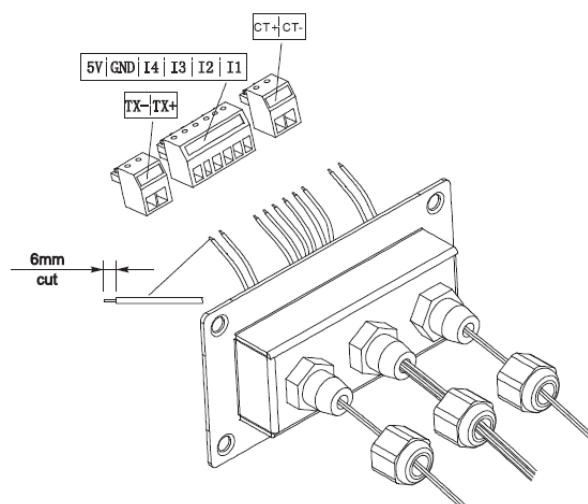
Inserimento dei cavi negli apposite passa cavo
